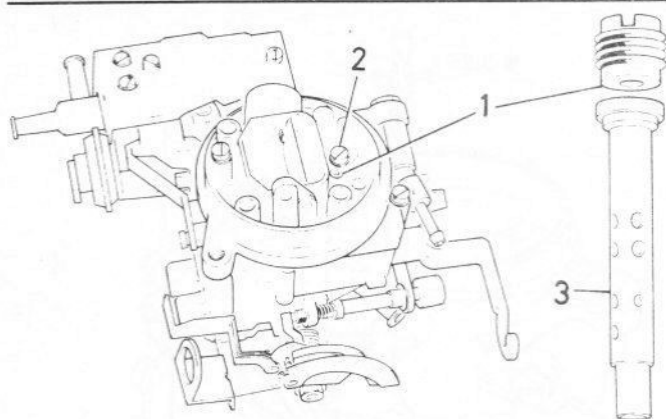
Vue d'en haut - carburateur Weber 36 TLC (Sec 8)
